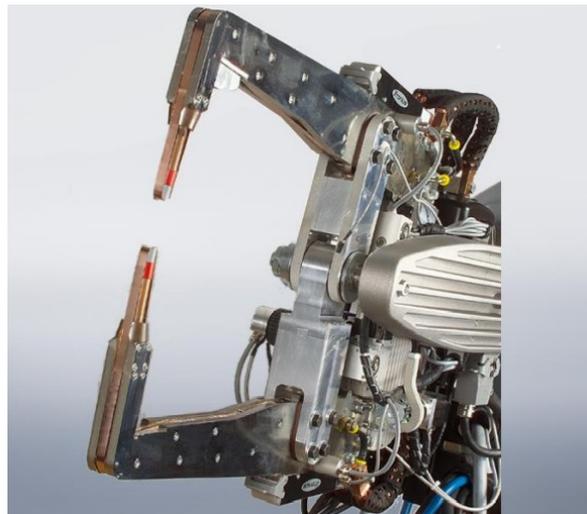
Máquina tipo C portátil para soldar por resistencia.
